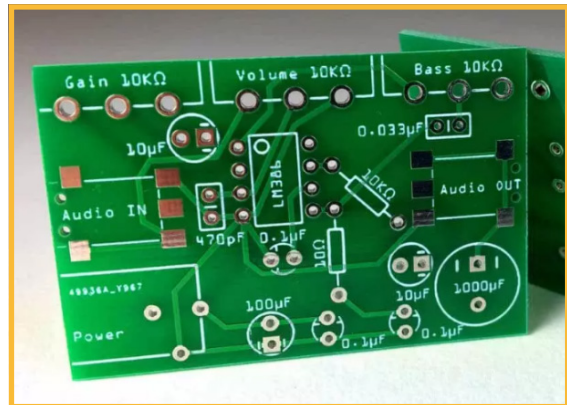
Placa PCB industrial. Fuente: Hardzone.
